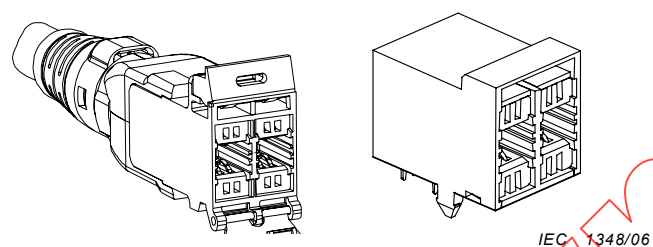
Vue isométrique d'embases de câble et de cartes imprimées
